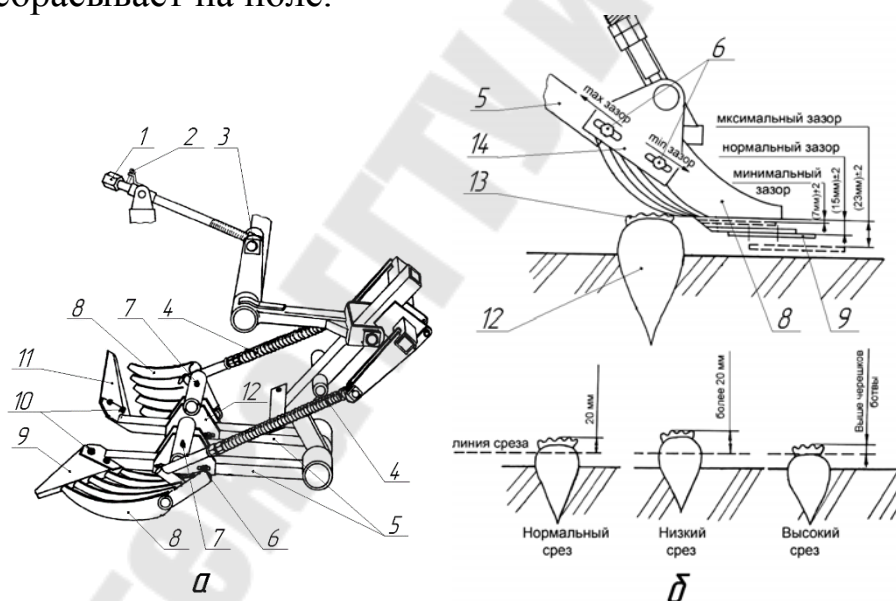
Дообрезчик корней: а – общий вид; б – схема регулировки высоты дообрезки головок свеклы; 1 – винт регулировочный; 2 – болт упорный; 3 – гайка специальная; 4 – пружина; 5 – держатель ножей; 6, 10 – болты; 7 – масленки; 8 – копиры; 9, 11 – ножи; 12 – корнеплод; 13 – черешки корня; 14 – опора ножа
